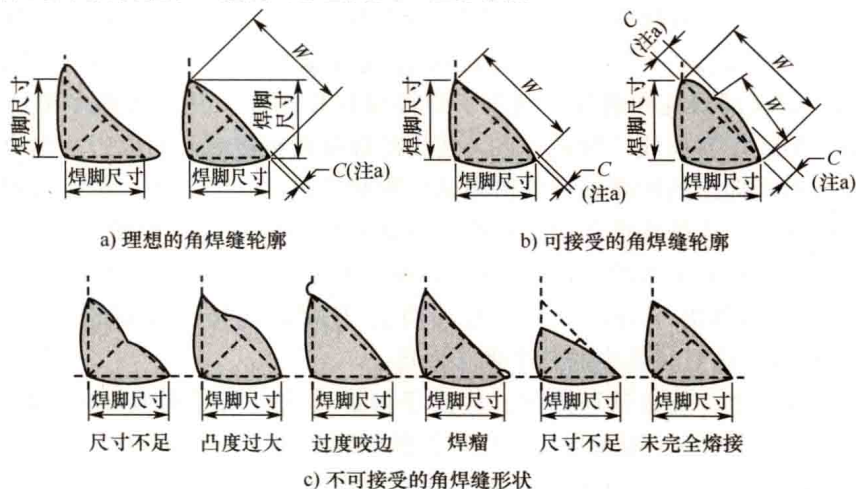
可接受和不可接受的焊缝形状。这是 AWS 结构钢焊接规程手册中的一页。如果你取一个焊过的接头并将它切割成两半，则会看到焊缝的轮廓。这种轮廓形状，本质上应是焊道的形状，它对于接头和结构的整体性是非常重要的。如你所见，一些焊缝形状是不可接受的，并且很可能导致焊缝失效而不能起到连接作用。
